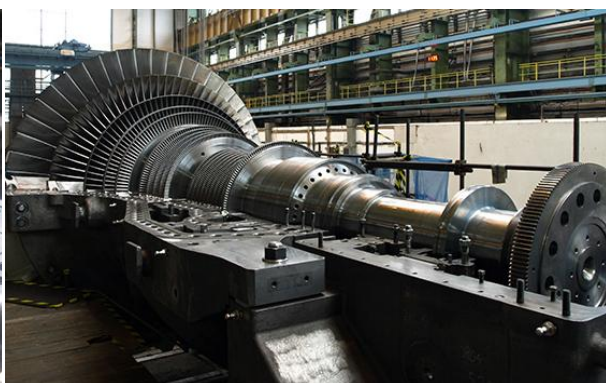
Rotor kondenzační turbíny [28]
